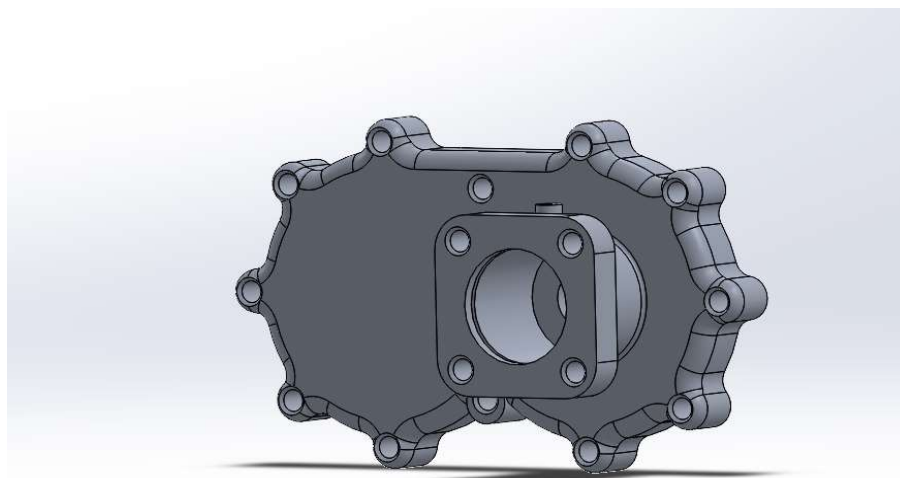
Ізометричний вид кришки корпусу.
